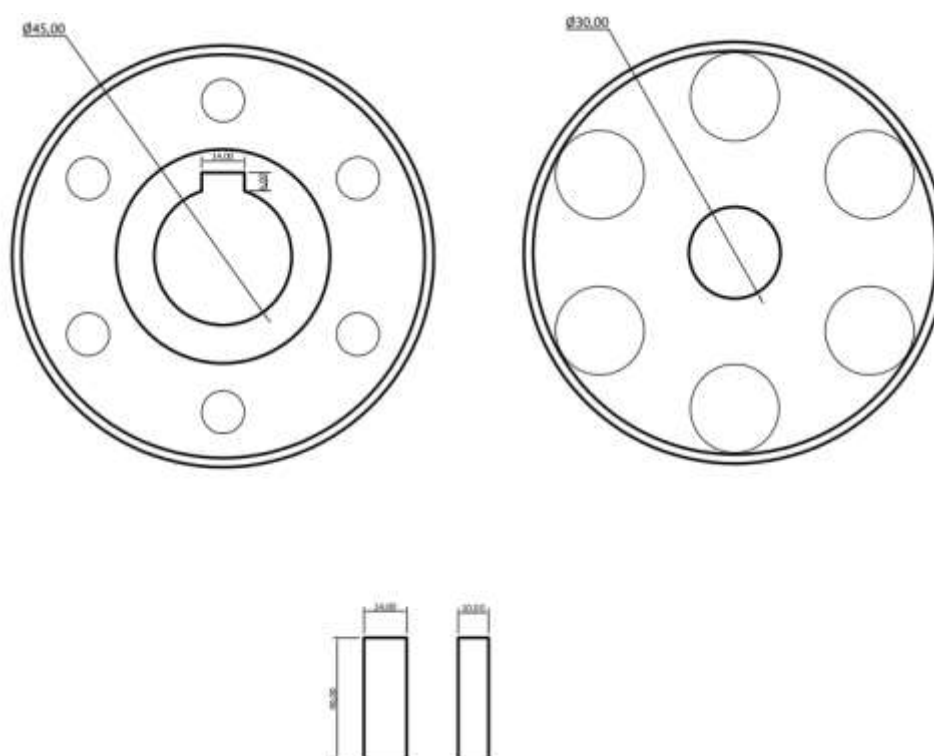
Креслення напiвмуфт для з'єднання двигунiв
